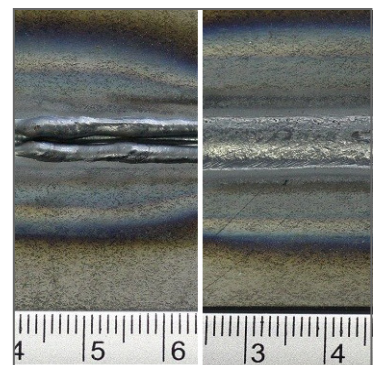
Plasmaschweißnaht (links) und Hybridschweißnaht (rechts)
